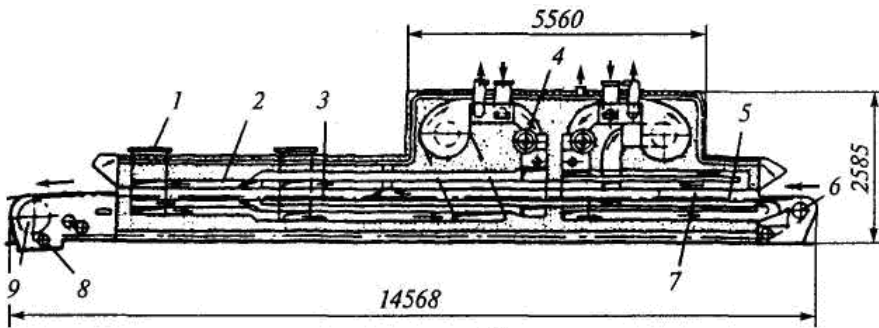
Піч ПХС-25М; 1 – витяжний канал; 2, 3 – верхній і нижній обігрівачі канали; 4 – топка; 5 – стрічкова черені; 6 – натяжний барабан; 7 – фартух; 8 – щітка; 9 – привідний барабан.
